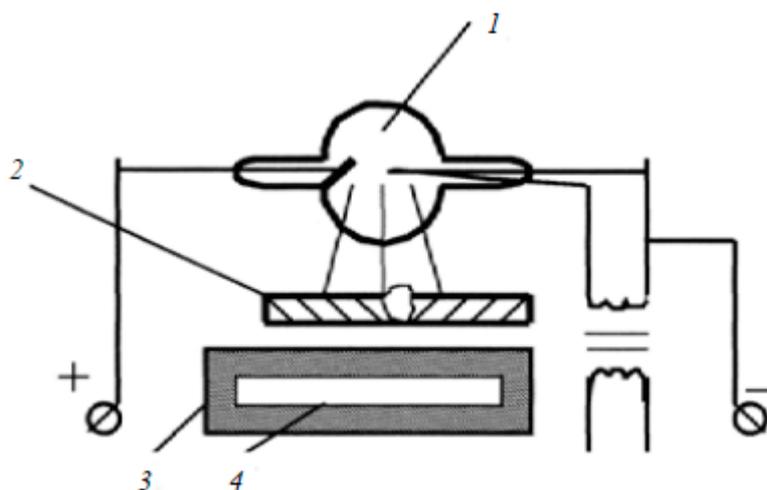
Рентгенографический контроль сварных соединений: 1 – рентгеновская трубка; 2 – сварное соединение; 3 – кассета; 4 – пленка
